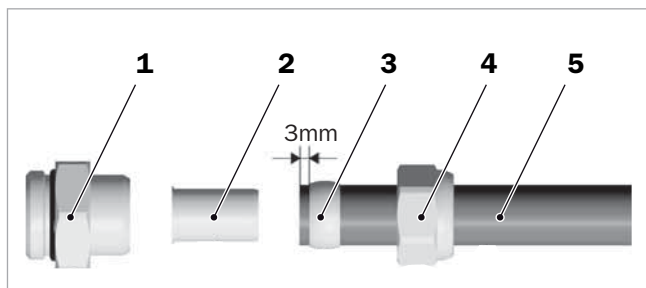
Montaggio del collegamento a vite con anello di bloccaggio
